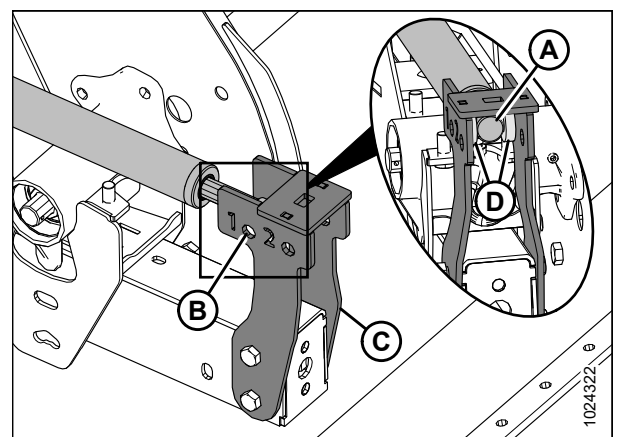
Rechter Haspel-Horizontalzylinder
